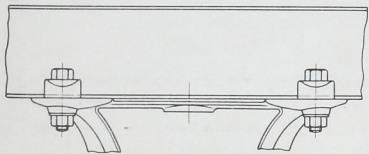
Befestigung der Lager mittels Klemmplatten.
